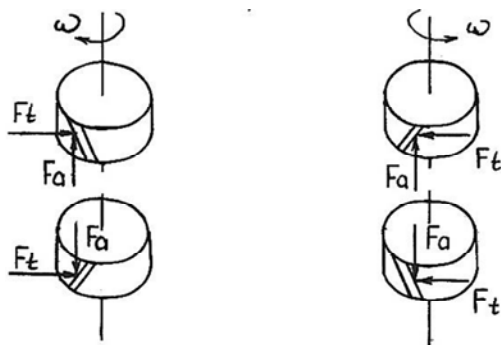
Направления сил на ведущем колесе косозубой передачи
